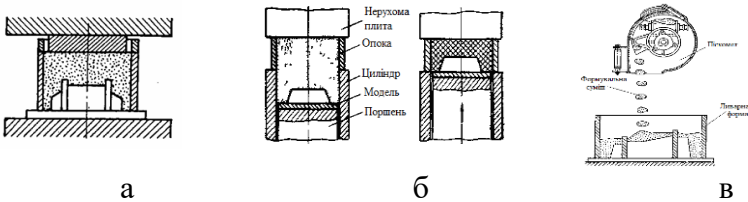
Машина з верхнім (а) та нижнім (б) пресуванням, формувальний піщомет для габаритних форм (в)
